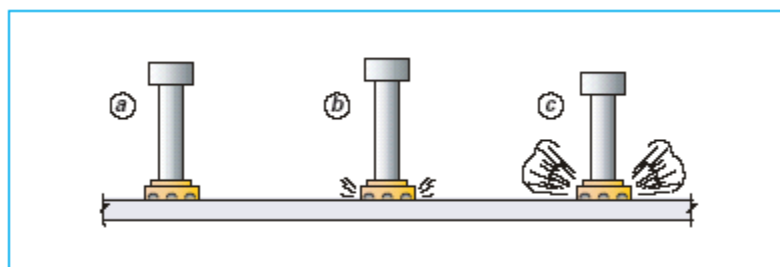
mise en œuvre des goujons soudés.
